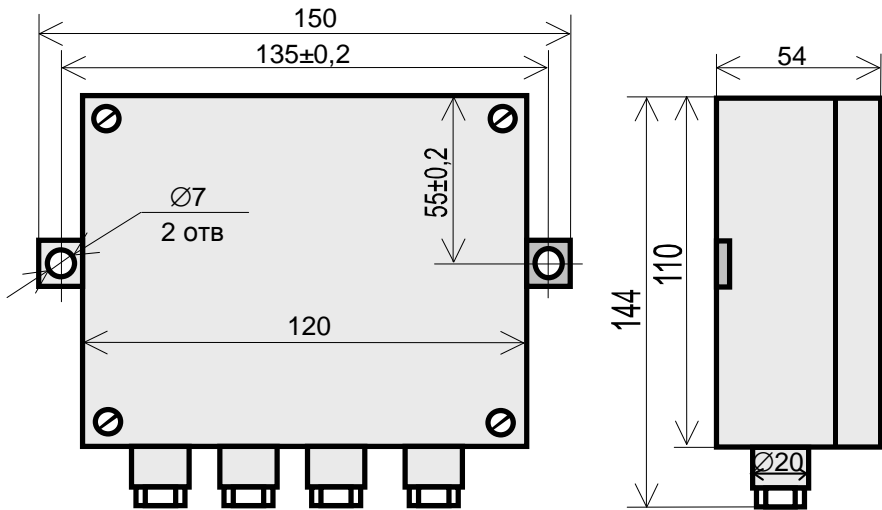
Габаритные и присоединительные размеры КБК и разветвителя
